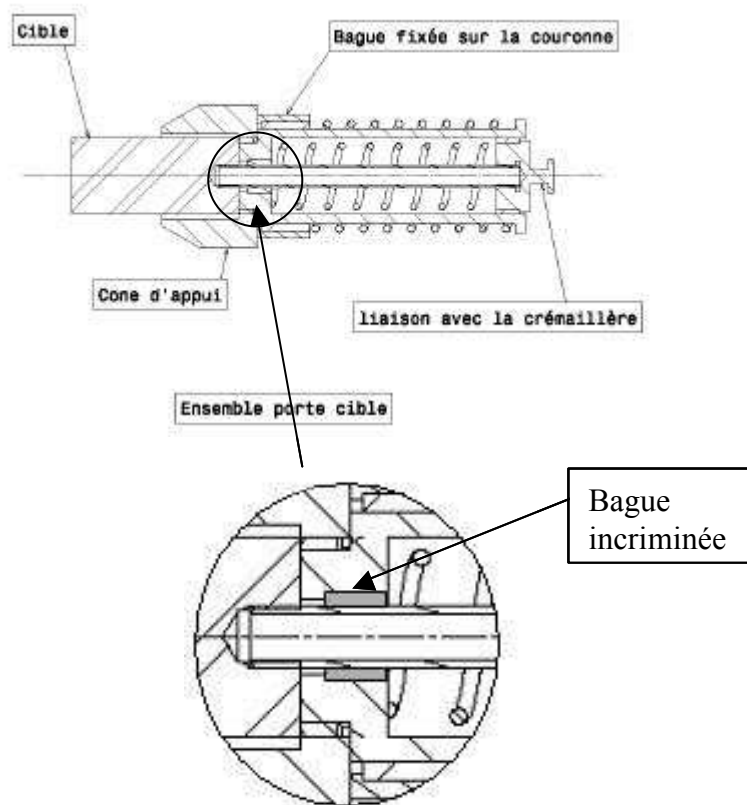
Ensemble porte-cible et lieu du grippage.
